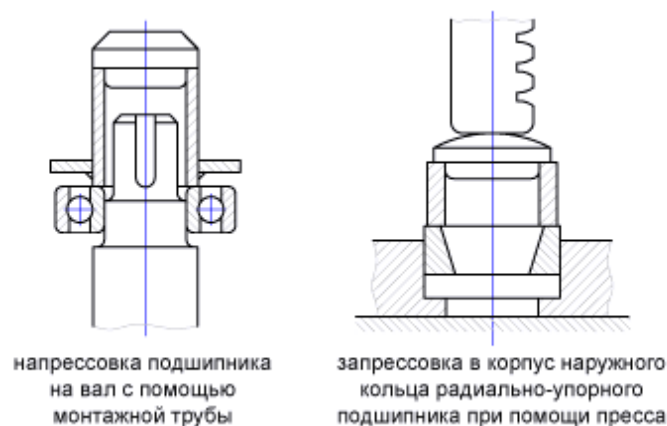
Запрессовка подшипника на вал и в корпус
